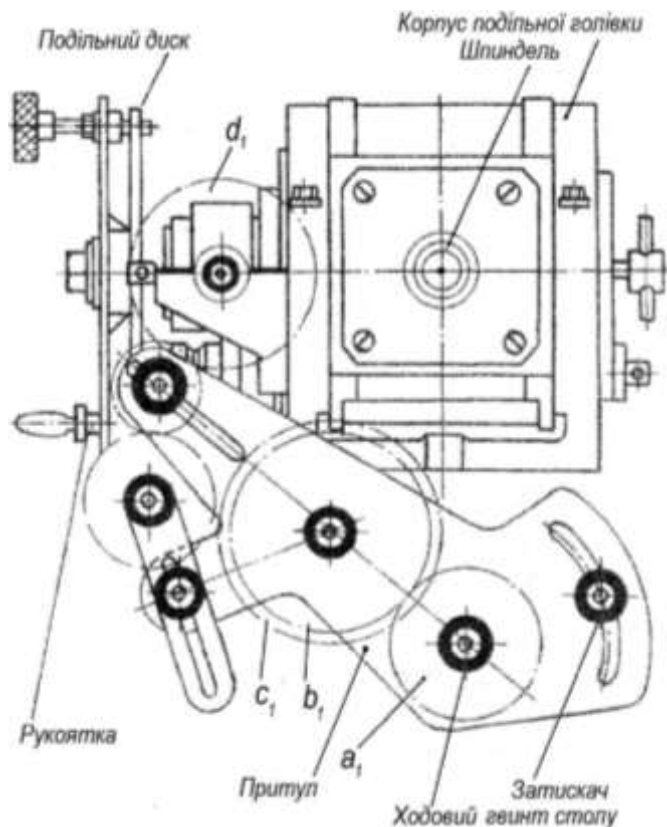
Змінні колеса універсально-фрезерного верстата
